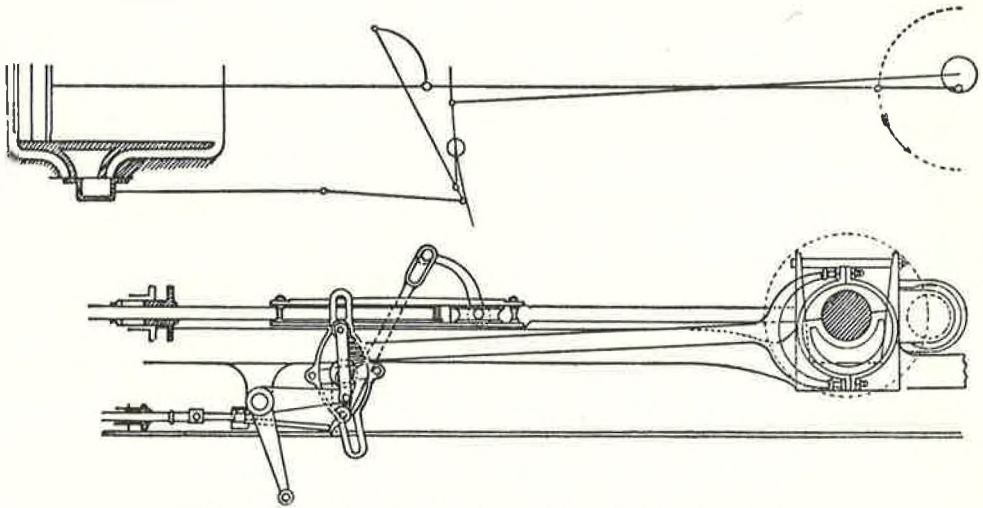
Dessin annexé au brevet belge du 5 octobre 1844.
